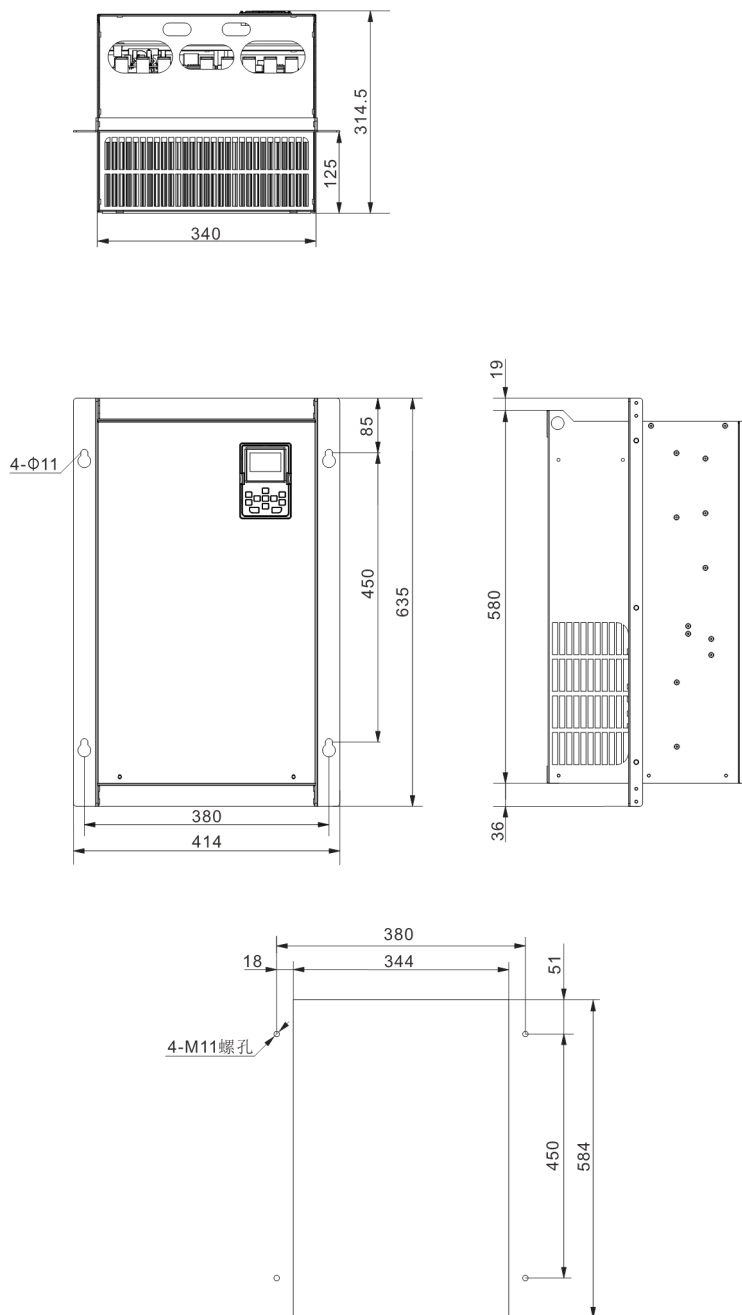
SIZE H(65-110kw)机型开孔尺寸
